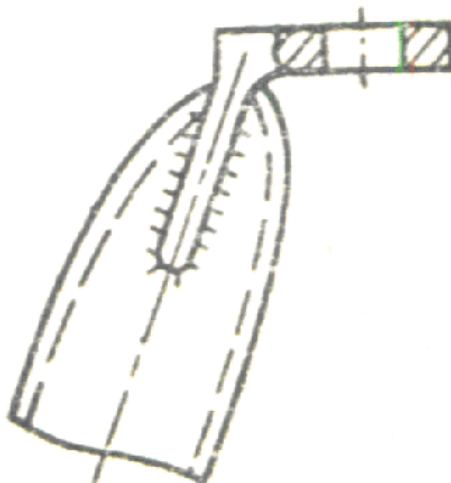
Конструкция соединения отрезка трубы с опорой
